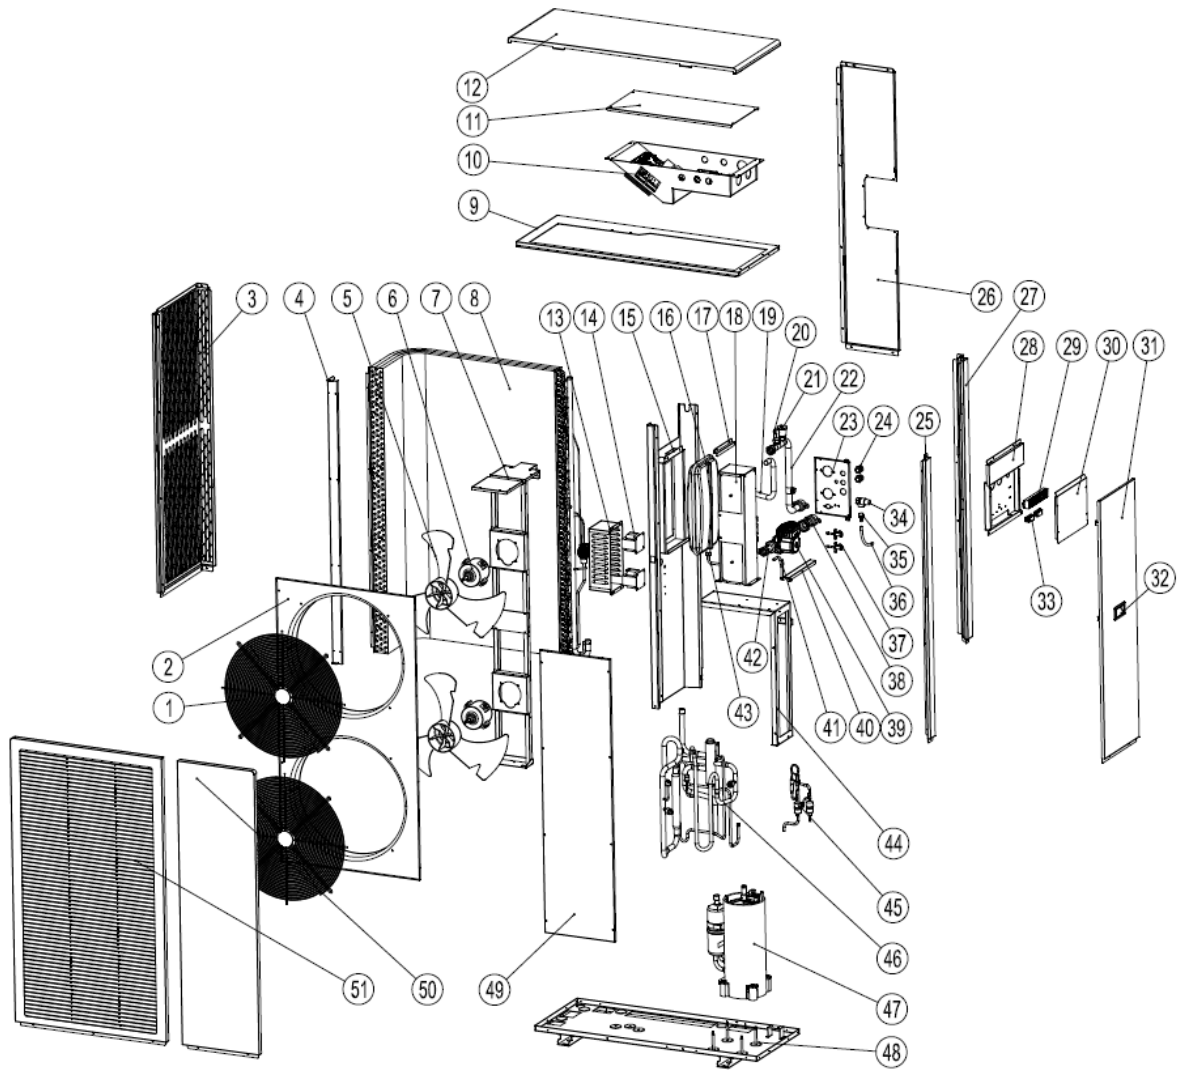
Explosionszeichnung der Wärmepumpe R2NT\_W\_22\_3P
